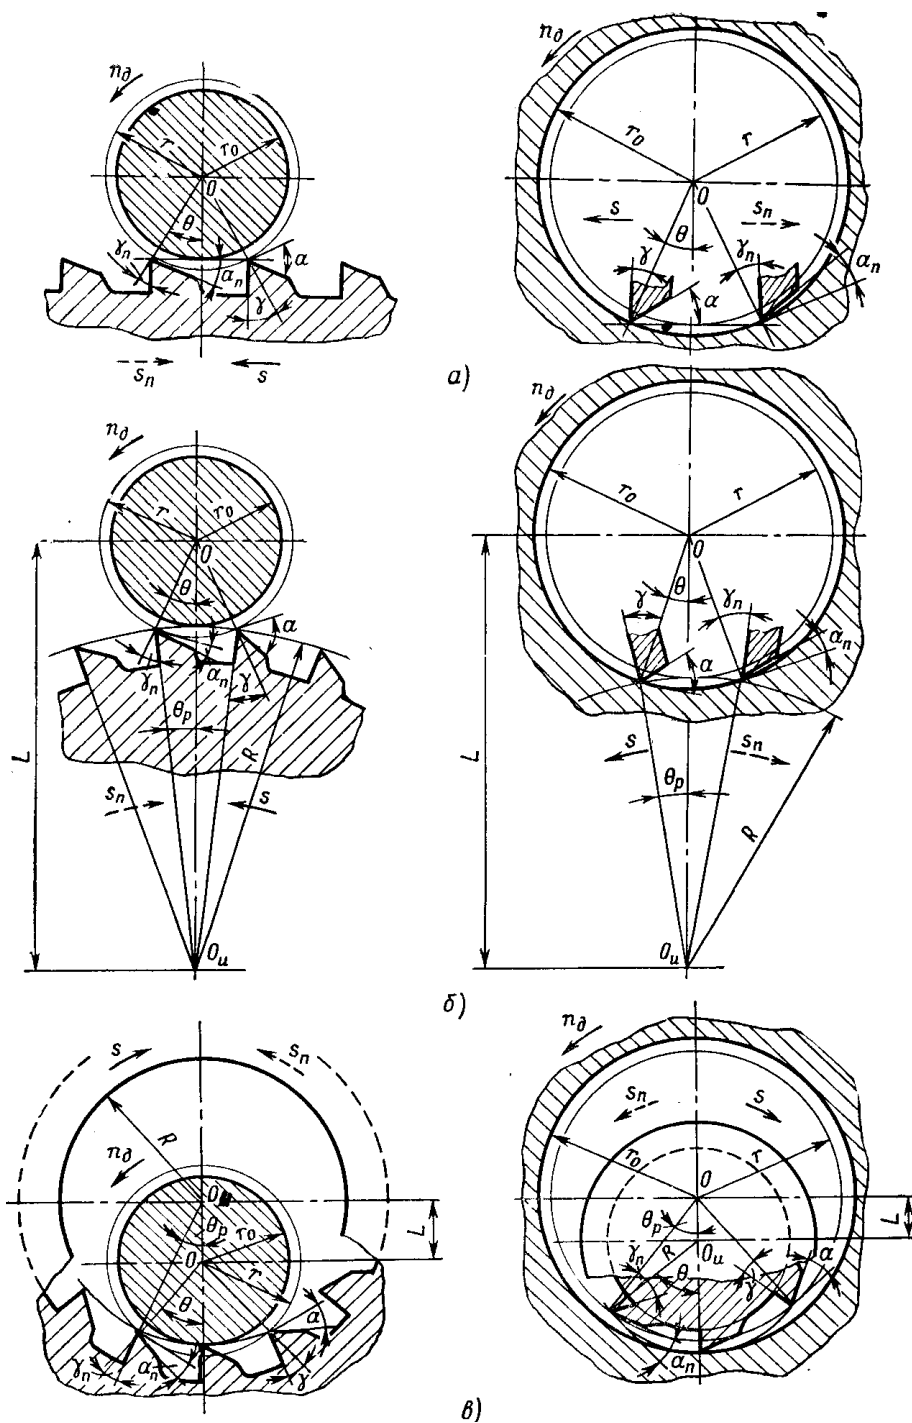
Схеми тангенціального точіння зовнішніх і внутрішніх поверхонь[9]:
